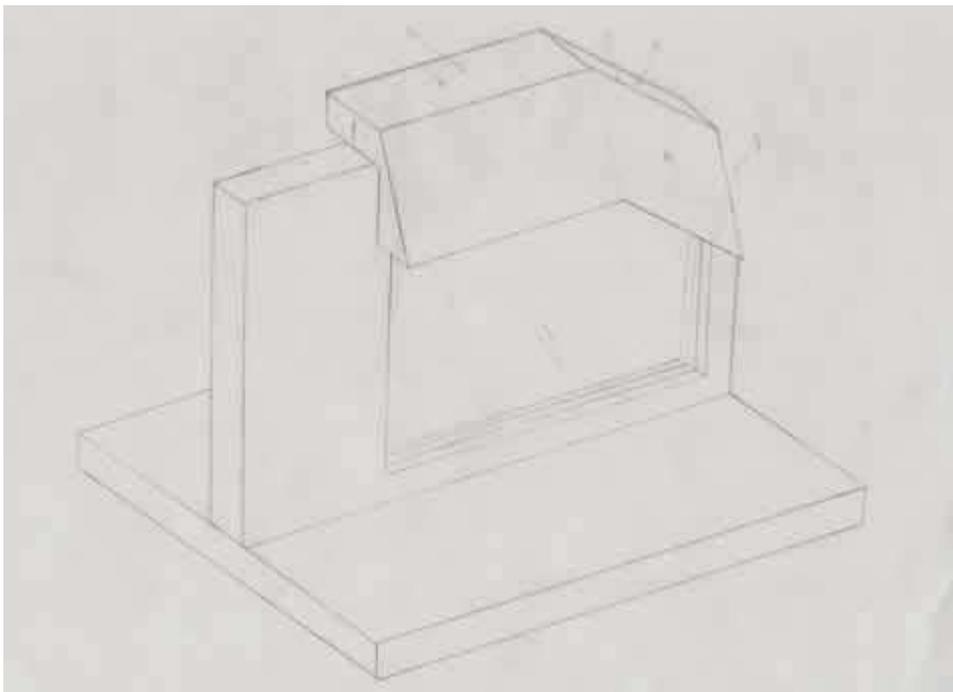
Projeto da porta em MDF com a calha acoplada. Fonte: Autores do projeto.
